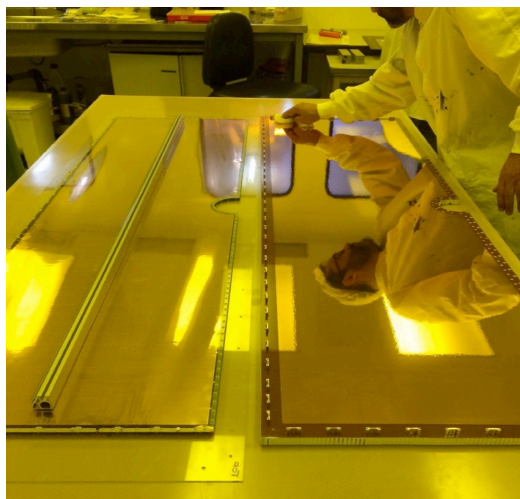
Изготовление детектора GEM размером $163 \times 39 \text{ см}^2$ в ЦЕРН.
